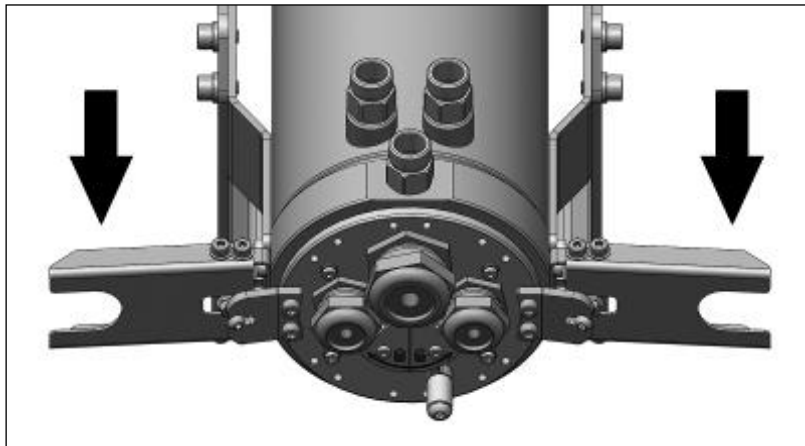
Rückansicht CoolingJacket mit Verriegelungshebel
